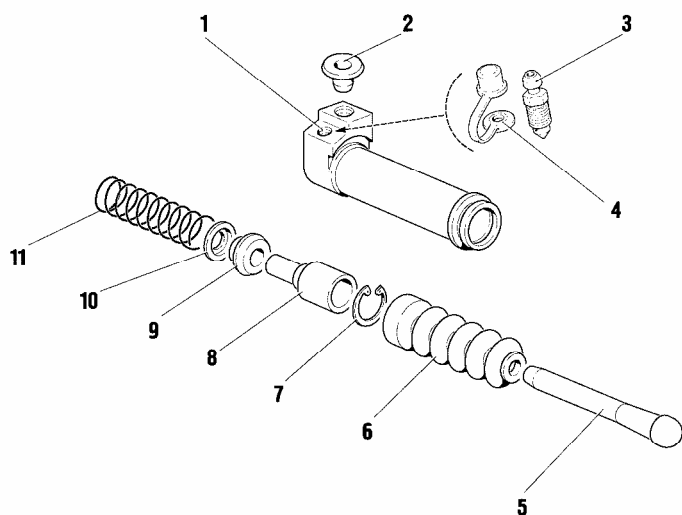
Детали цилиндра привода выключения сцепления (рабочего цилиндра):
